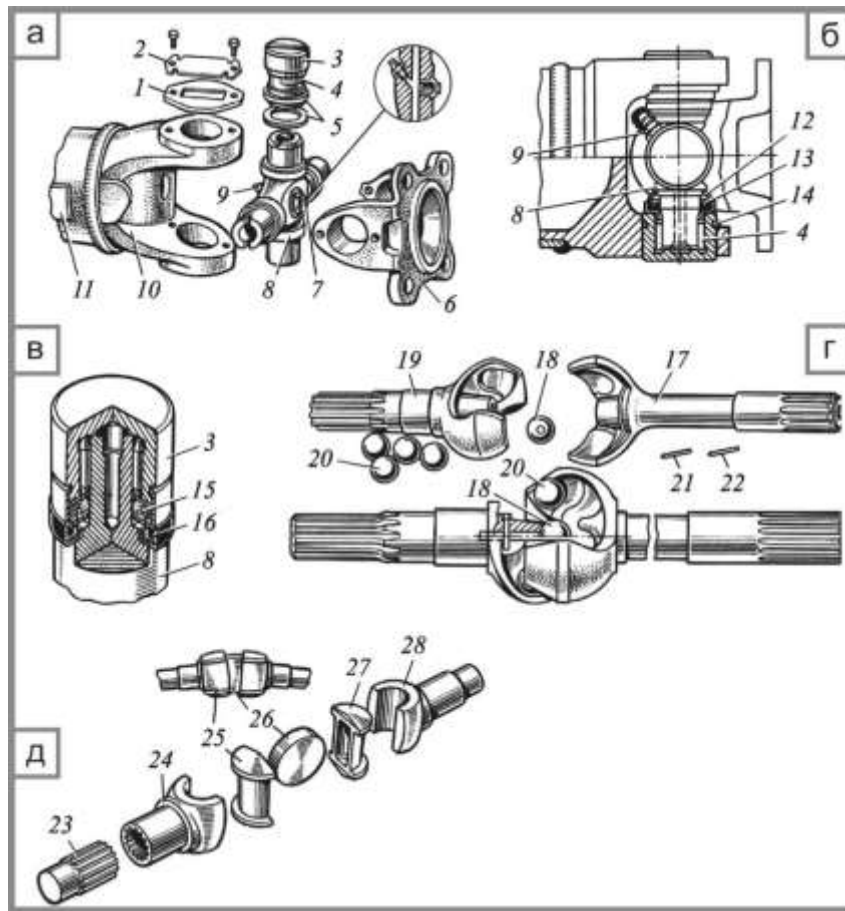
Деталі карданних шарнiрiв несталих (а – в) та сталех (г – д) кутових швидкостей: 1 – кришка; 2 – стопорна пластина; 3 – стакан пiдшипника; 4 – голки; 5 – повстянi манжети; 6, 10, 24, 28 – вилки; 7 – запобiжний клапан; 8 – хрестовина; 9 – маслянка; 11 – карданний вал; 12 – вiдбивач; 13 – самопiдтискна манжета; 14 – стопорне кiльце; 15, 16 – манжети радiального i торцевого ущiльнень; 17 – внутрiшнiй кулак; 18 – центральна кулька; 19 – зовнiшнiй кулак; 20 – ведучi кульки; 21 – штифт; 22 – шпилька; 23 – пiввiсь; 25, 27 – напiвцилiндричнi кулаки; 26 – центральний диск
